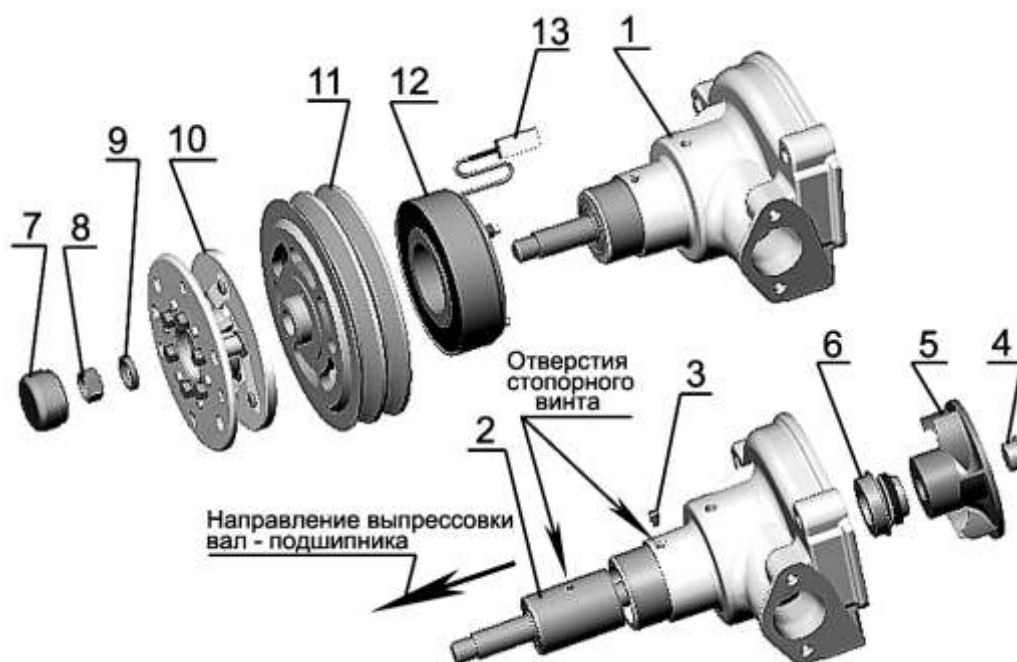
а – Водяной насос с электромагнитной муфтой вентилятора: 1 – корпус; 2 – вал-подшипник; 3 – винт стопорный; 4 – заглушка; 5 – крыльчатка; 6 - уплотнение водяного насоса SP/1341; 7 – колпачек; 8 – гайка; 9 – шайба; 10 – корпус вентилятора; 11 – шкив; 12 – электромагнит с фланцем; 13 – штекерный разъем
